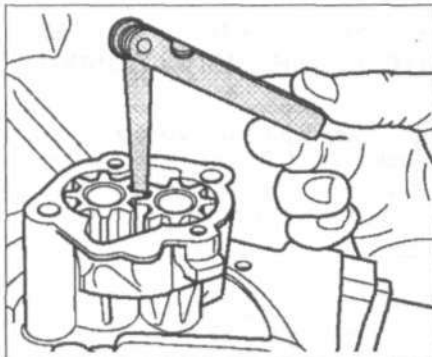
Проверка зазора между шестернями насоса с помощью щупа.
